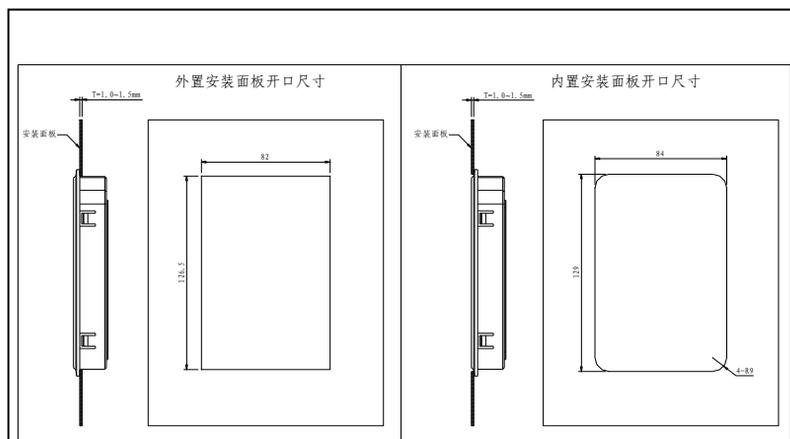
：键盘安装开口尺寸图(尺寸单位：mm)
